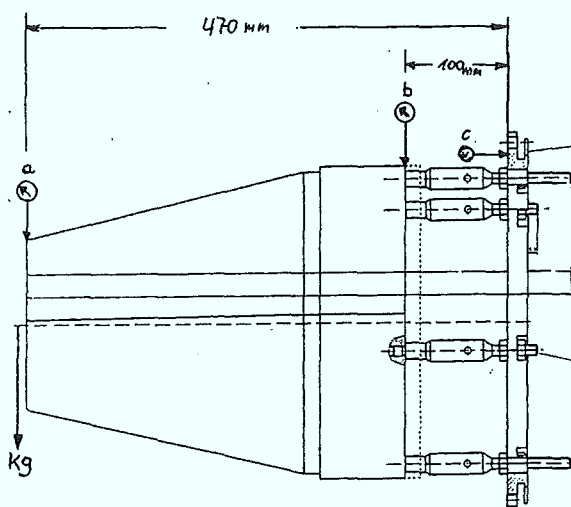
Zeichnung des BGO-Detektors mit Skizze des Verformungstests.
